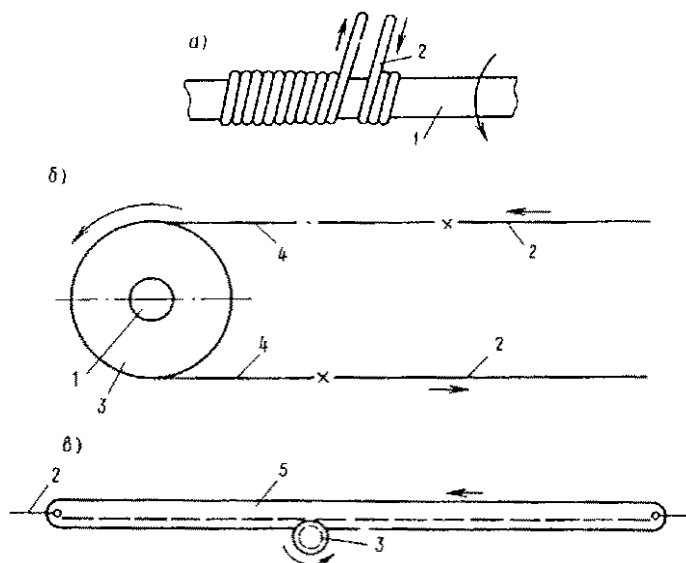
Способы передачи усилия от приводного вала к приводным тросам: а – передача «вал - трос»; б – цепная передача; в – реечная передача; 1 – приводной вал; 2 – приводной трос; 3 – шестерня; 4 – цепь; 5 – рейка
